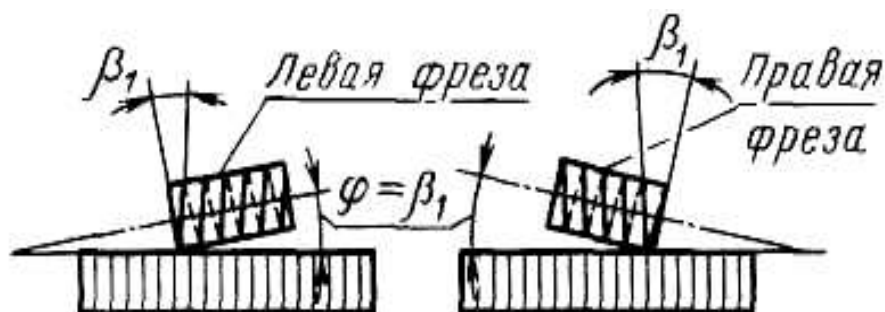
Расположение червячной фрезы при зубофрезеровании прямозубого колеса
